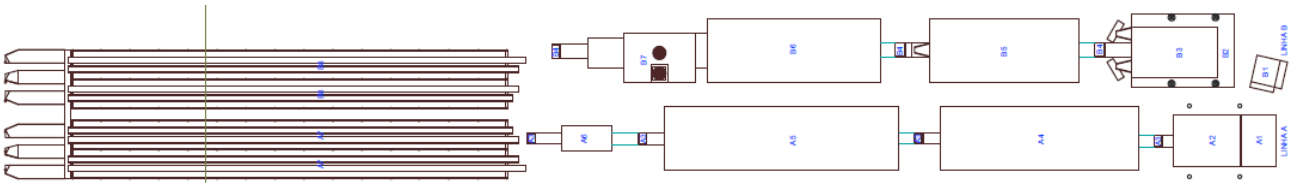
Layout das linhas de fabricação A e B e dos silos.
